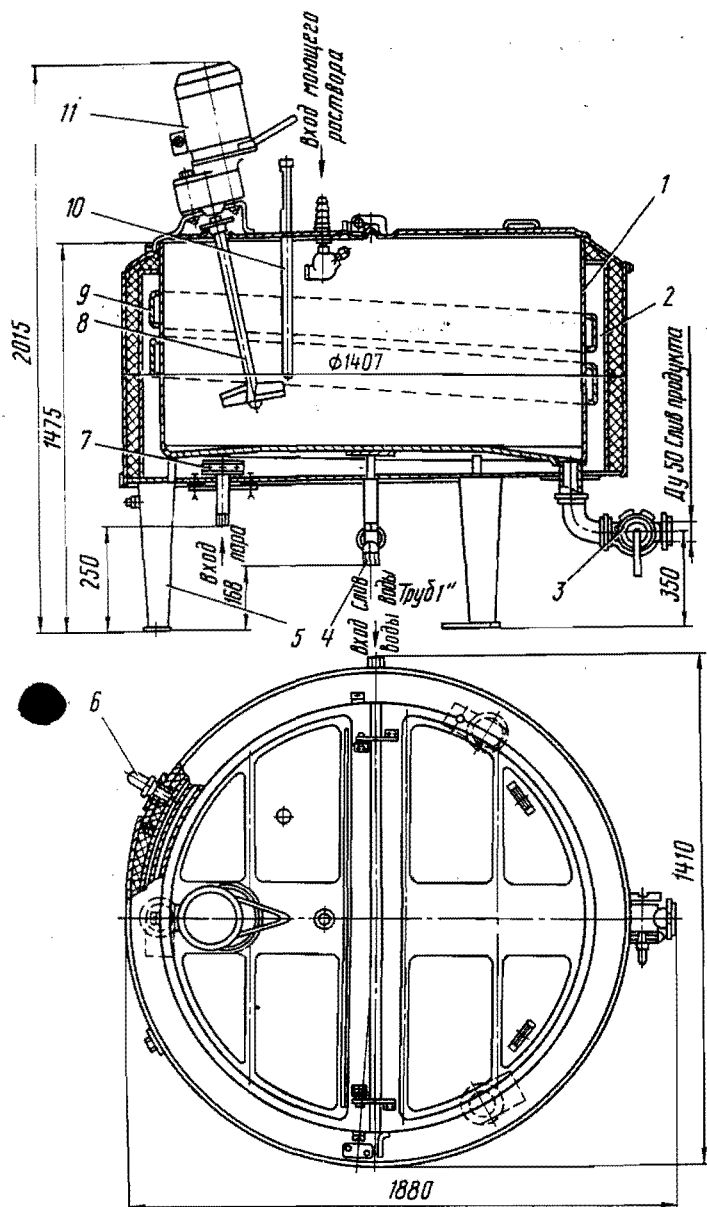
Общий вид резервуара универсального марки Г2-ОТ2-А:
